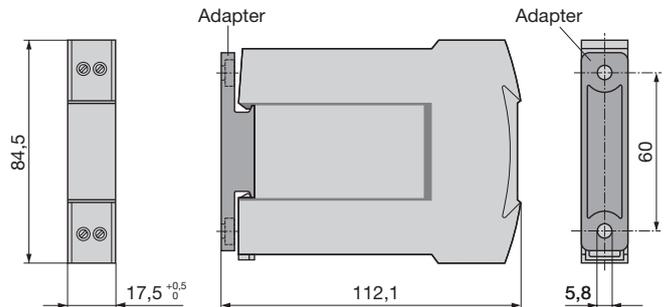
SINEAX TI 807-5.... (N17-Gehäuse) mit Adapter für direkte Wandmontage.
